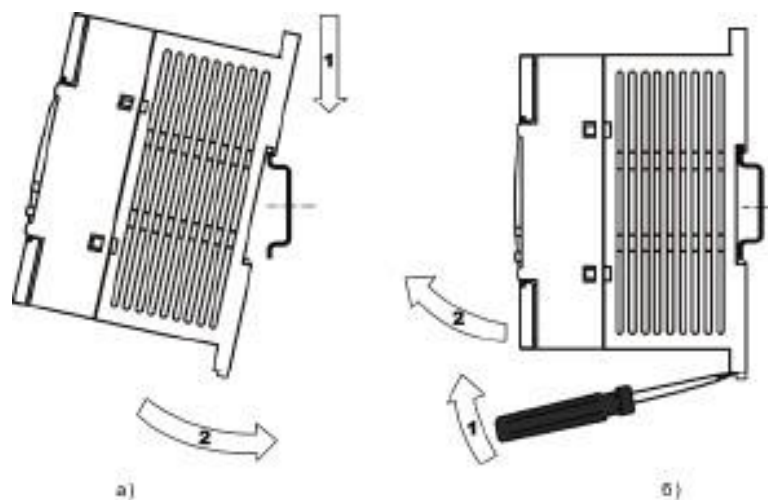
а) – Установка контролера на DIN-рейку; б) – зняття контролера з DIN-рейки
